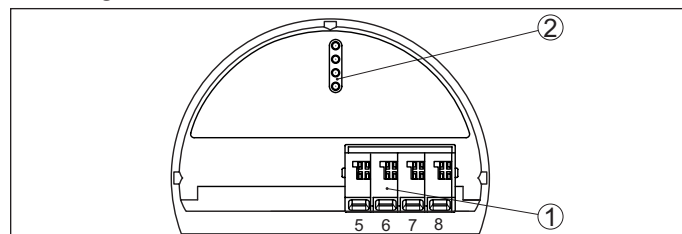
Bedienings- en aansluitruimte bij niet-Ex instrumenten en instrumenten met niet-intrinsiek veilige signaaluitgang
